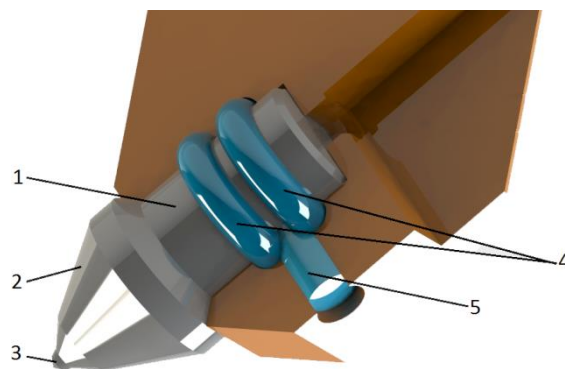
Конструкция поворотных резцов: 1 – хвостовик резца; 2 – головка резца; 3 – твердосплавный наконечник; 4 – полимерный материал; 5 – отверстие для заливки
